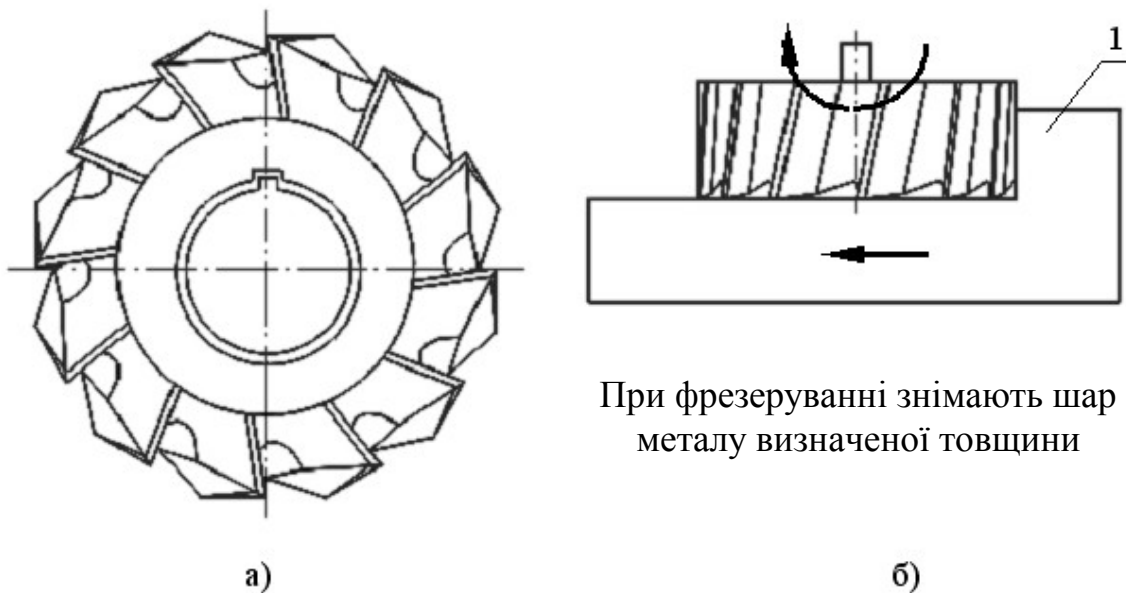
Торцева фреза (а) і обробка плоскої заготовки (б):
